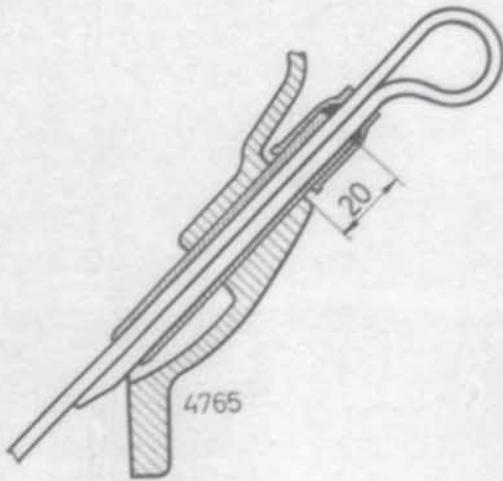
Einbau des Führungsrohres zum Ölmeßstab F 1L 712
